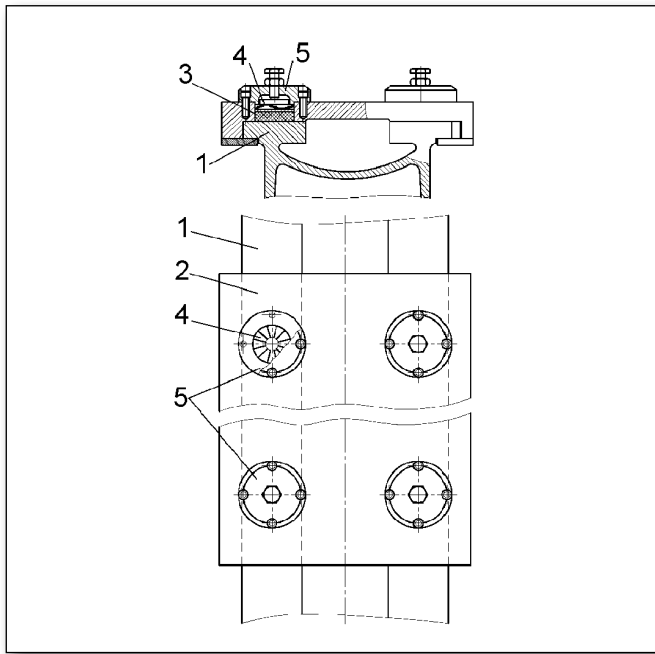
Устройство для разгрузки направляющих стола: 1 — станина; 2 — стол; 3 — антифрикционный вкладыш; 4 — пружина; 5 — крышка.
